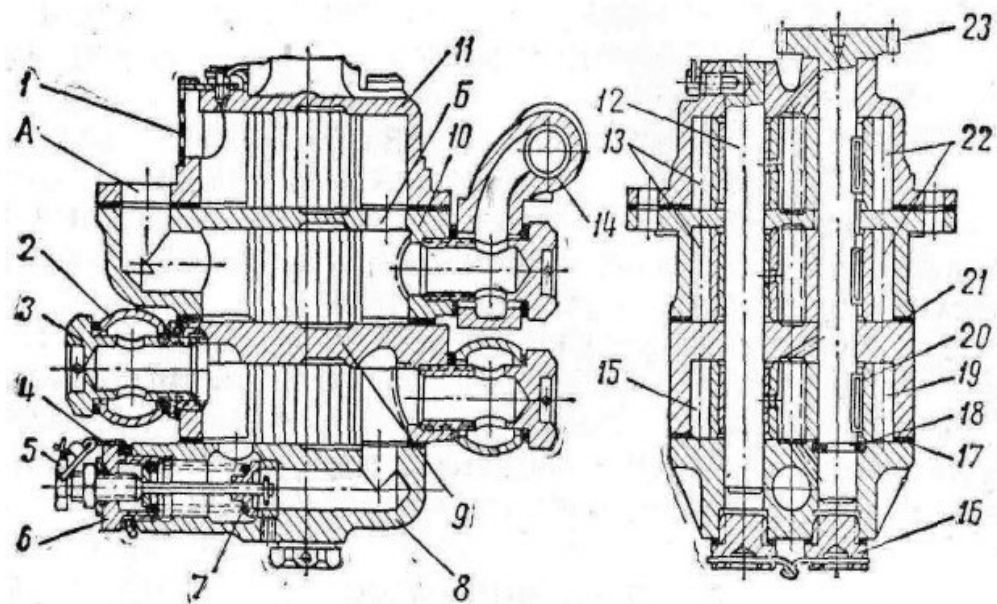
Масляний насос: 1 – сітка; 2 – наконечник; 3 – затиск; 4 – пластинчастий замок редукційного клапана; 5 – стрижень редукційного клапана; 6 – корпус редукційного клапана, 7 – тарілка редукційного клапана, 8 – кришка; 9 – корпус нагнітаючої секції; 10 – корпус нижньої відкачуваючої секції; 11 – корпус верхньої відкачуваючої секції; 12 – вісь ведених шестірень; 13 – ведомі шестерні відкачуючих секцій, 14 – коробки відводу масла в систему; 15 – ведена шестерня нагнітаючої секції; 16 – пробка, 17, 21 – прокладки; 18 – стопорне кільце; 19 – ведуча шестерня нагнітаючої секції; 20 – шпонка; 22 – ведучі шестерні відкачуючих секцій; 23 – ведучий вал з шестернею; Б – отвір, що з'єднує нагнітальні камери відкачуючих секцій; А – усмоктувальний отвір нижньої відкачуваючої секції
